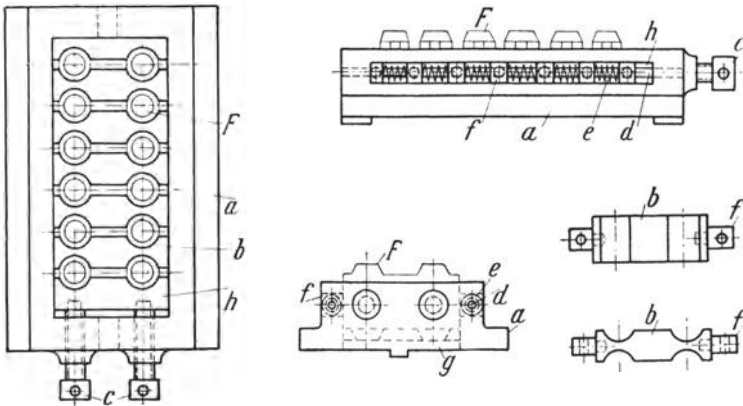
Spannvorrichtung zum Fräsen von Formstücken.
